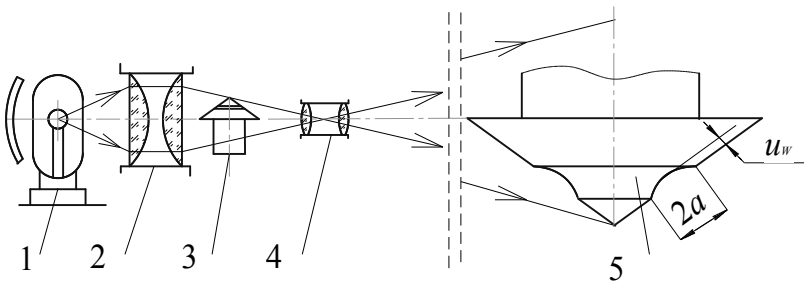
Схема вимірювання форми і глибини зношеної поверхні:
